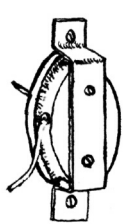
Vorschlag für die Befestigung der Kopfhörerkapsel am Chassis.
